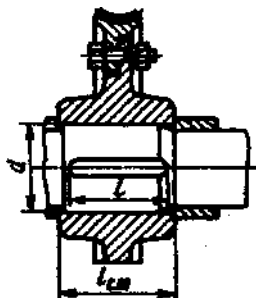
Шпоночное соединение червячного колеса с валом
